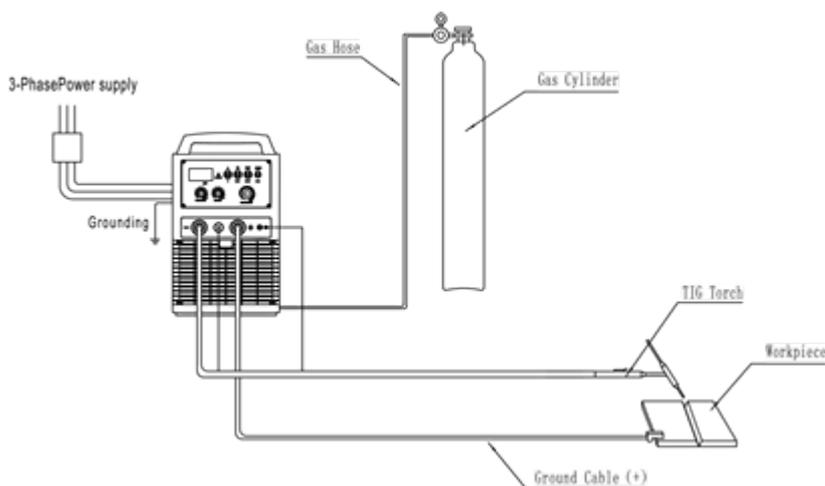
TIG сварка (стандартная)
